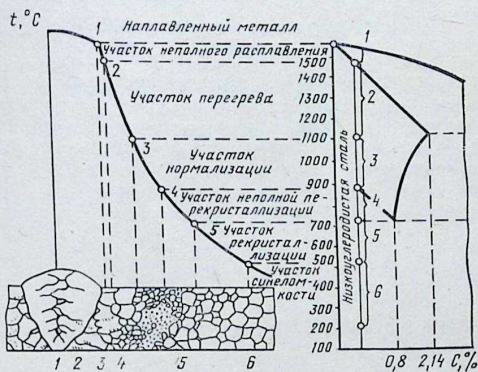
Схема строения стыкового сварного соединения.
